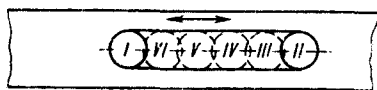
Порядок выборки гнезда на сверлильно-пазовальном станке с ручной подачей спиральным сверлом и концевой фрезой
